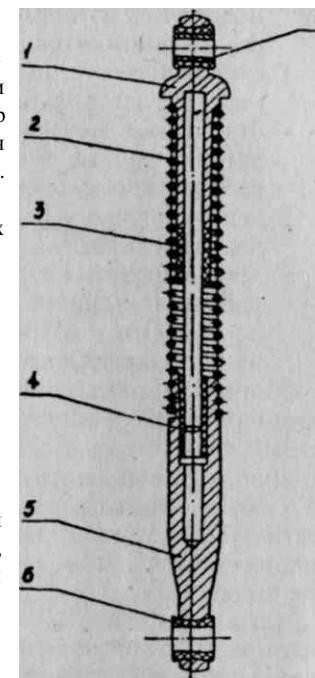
Амортизатор задний: 1 - головка со штоком; 2 - пружина; 3 - буфер; 4 - втулка; 5 - корпус в сборе; 6 - вкладыш; 7 - втулка
